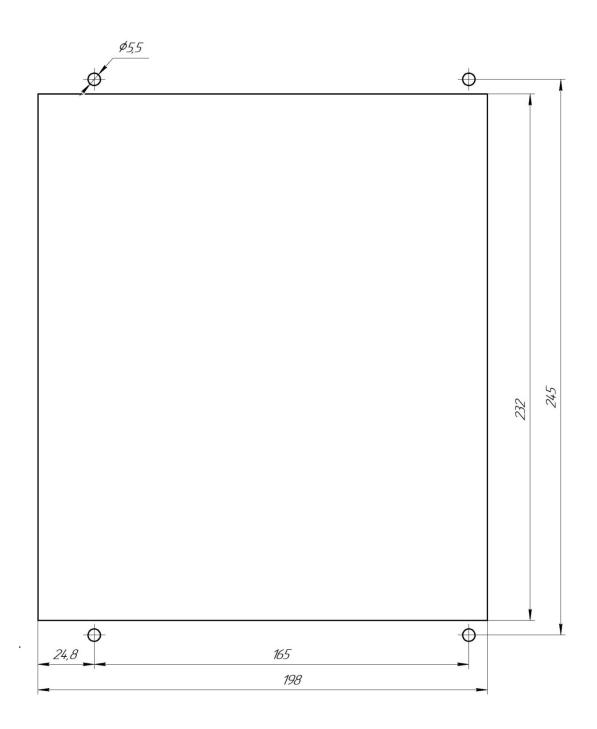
Габаритные размеры окна и крепежных отверстий для установки устройств Р3Л-05.Ф5, Р3Л-05.Ф6
